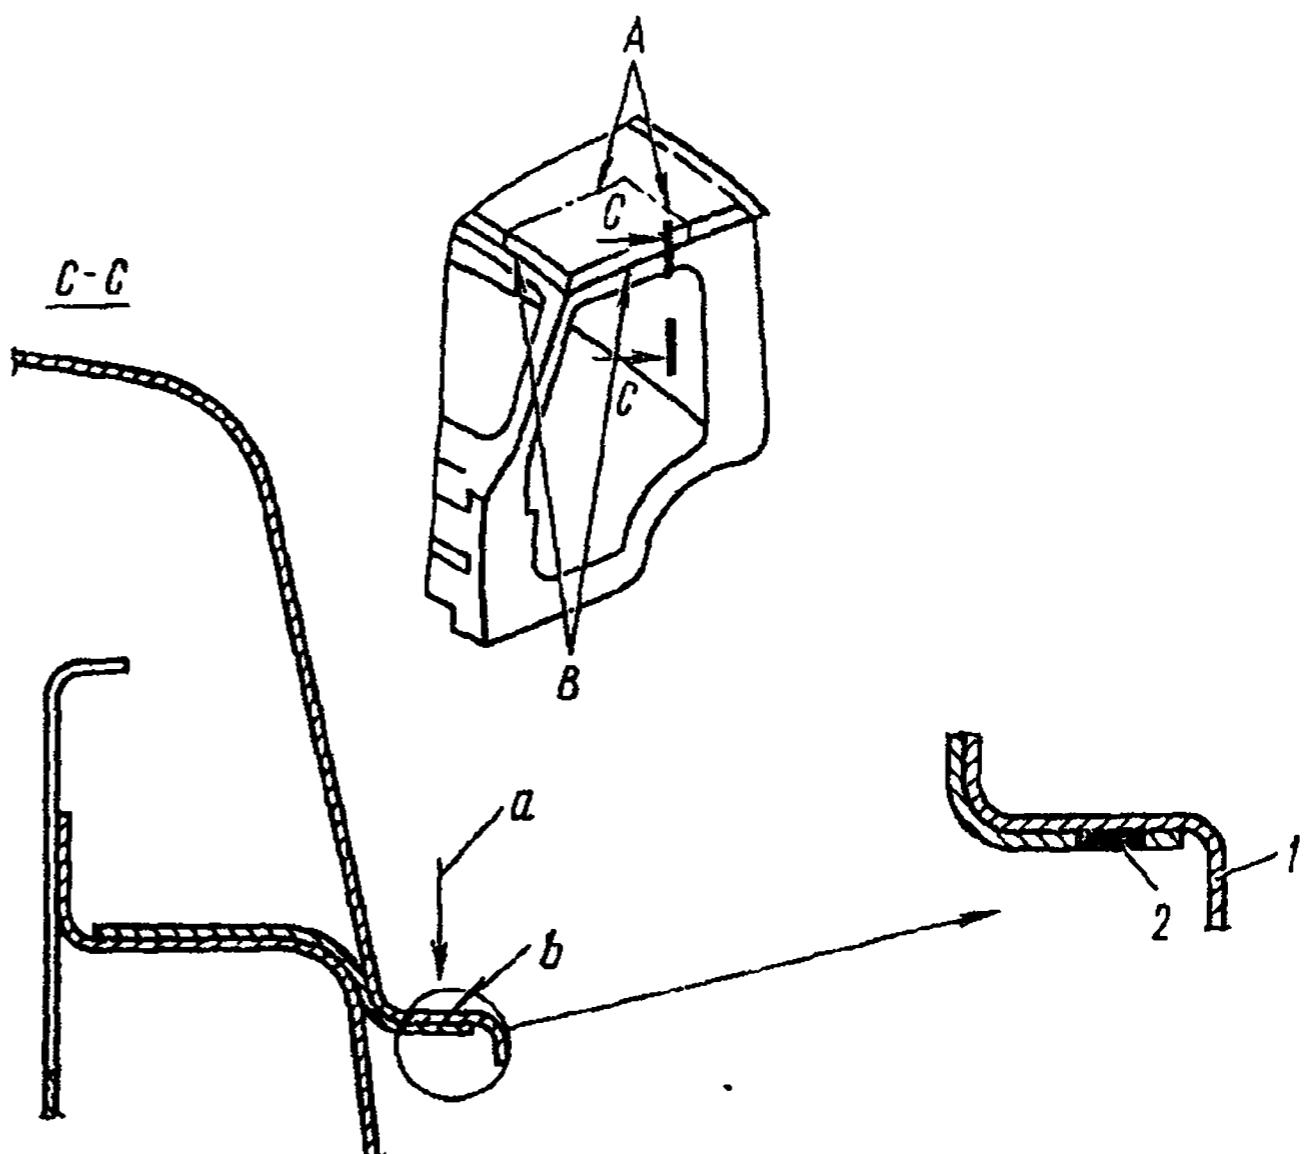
Места отсоединения дефектных деталей и способ приварки ремонтных деталей:
